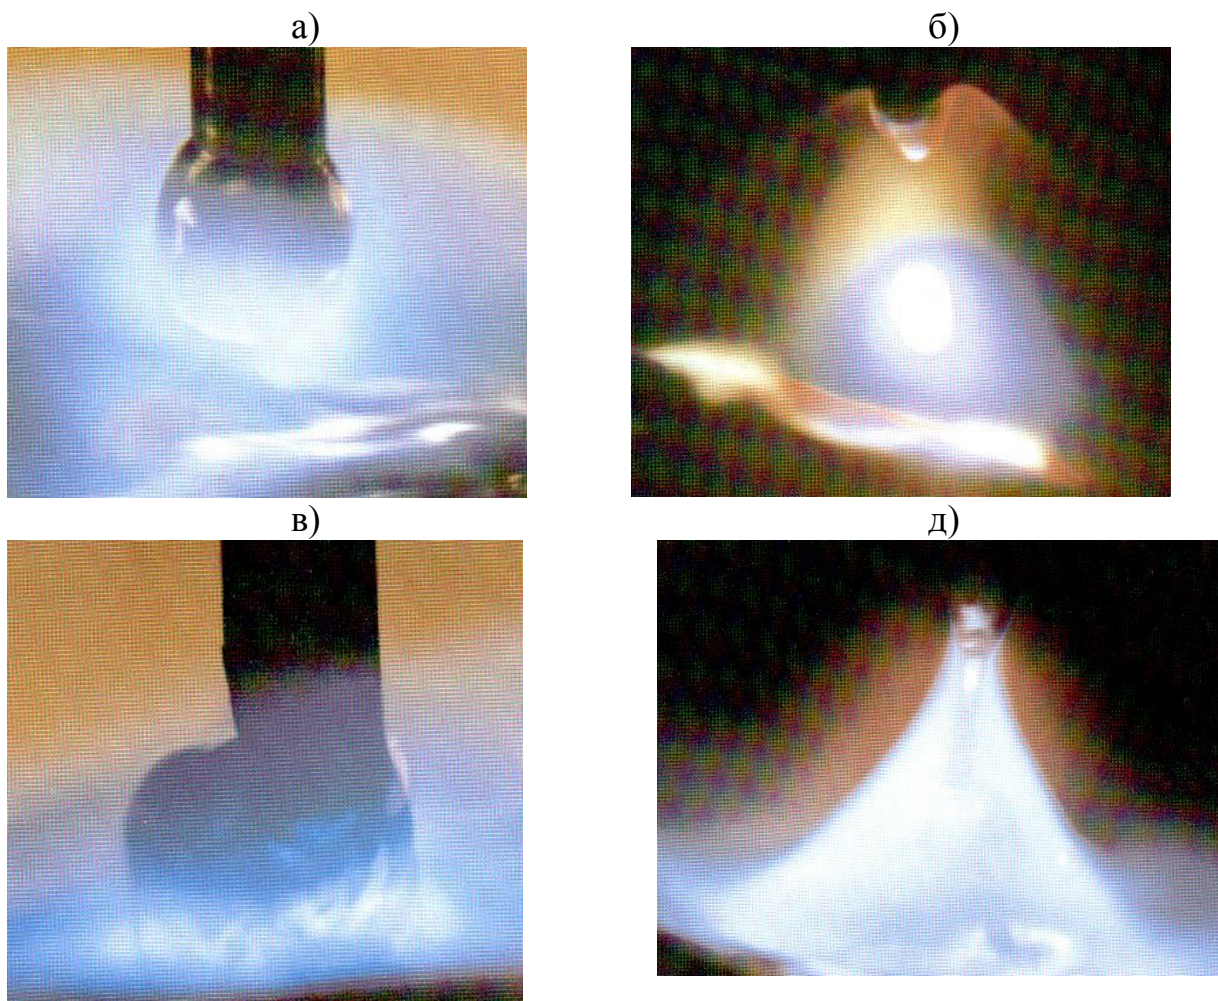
Сварочная дуга при различных типах переноса металла:
